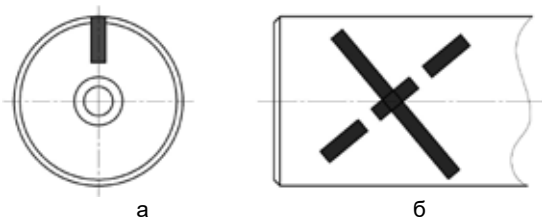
Примеры нанесения меток на торцевую (а) и боковую(б) поверхности свободного конца вала.
